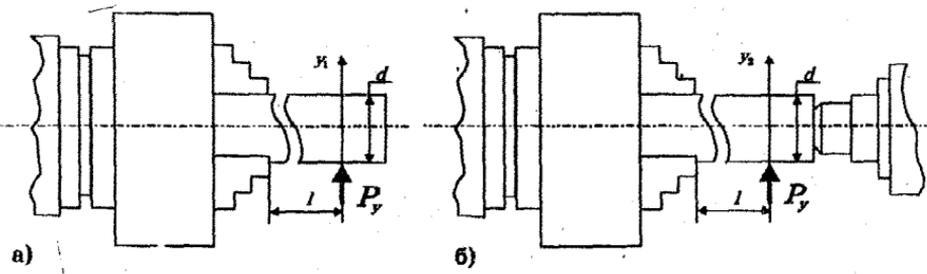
Схема моделирования упругих деформаций технологической системы станка 16К20: а) заготовка консольная; б) заготовка поджата центром
